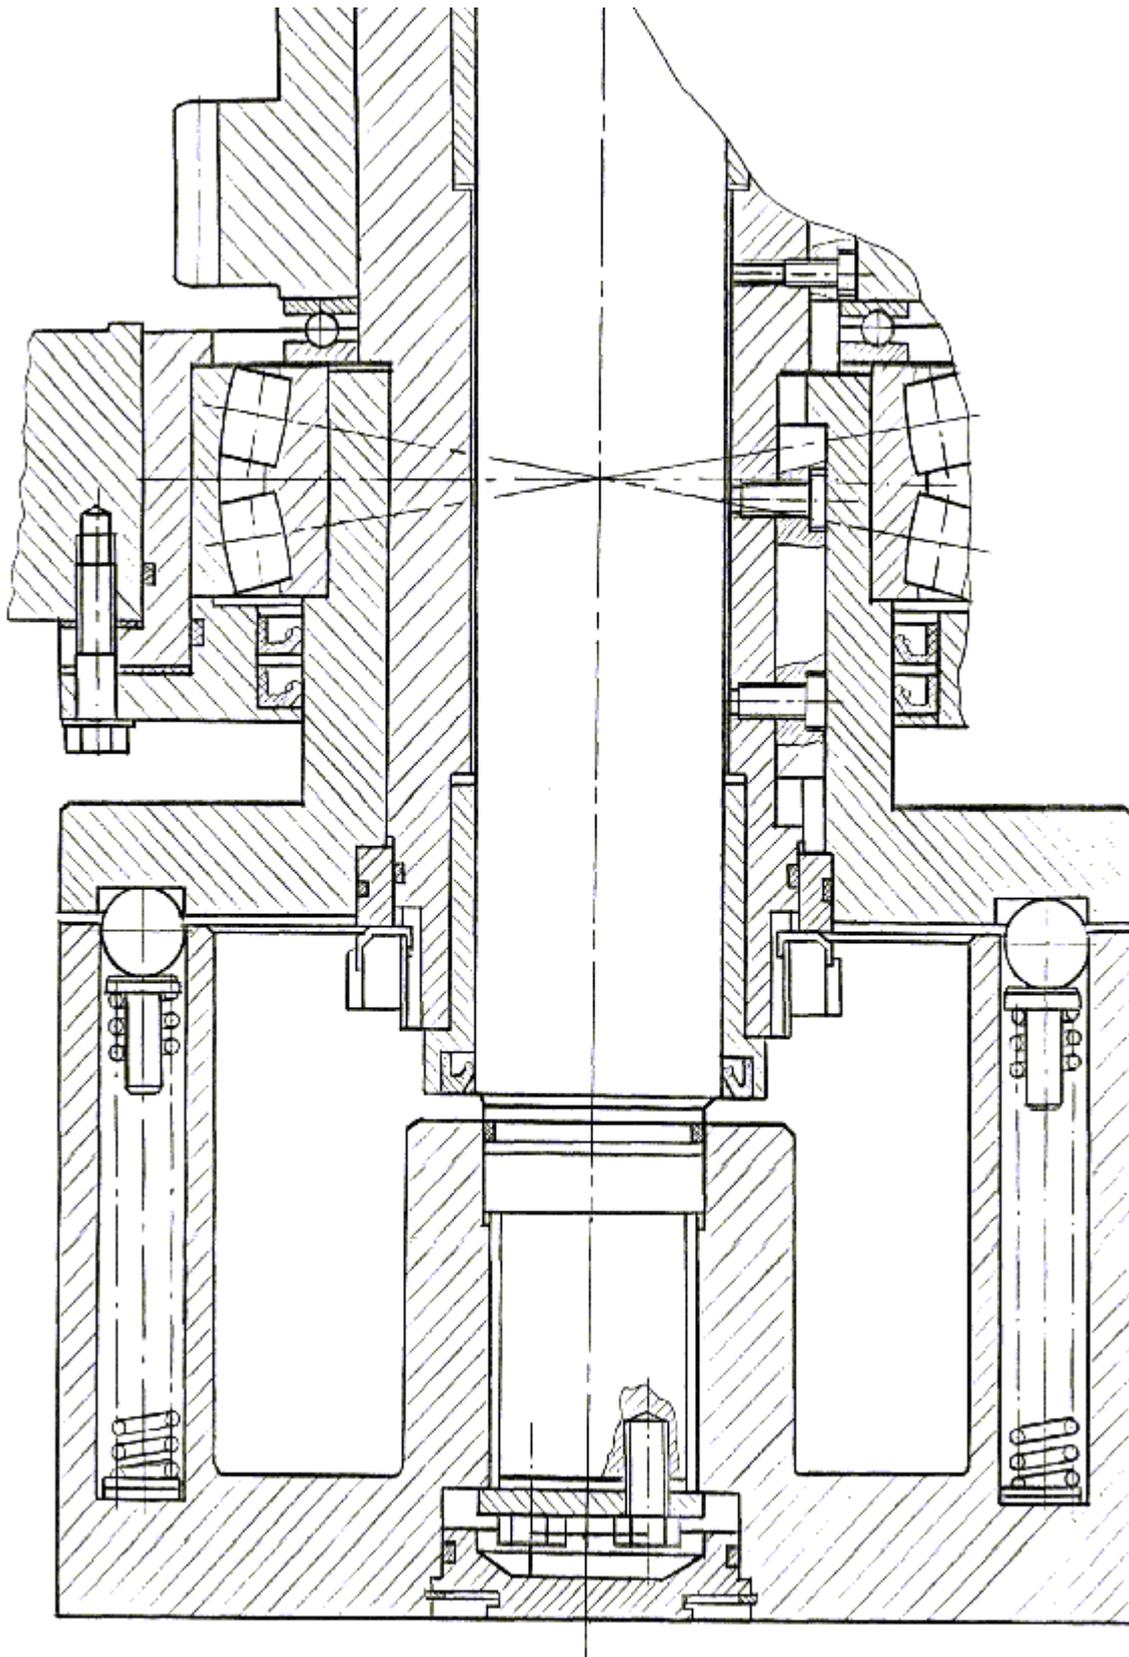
Конструкция шариковой предохранительной муфты на валу редуктора
